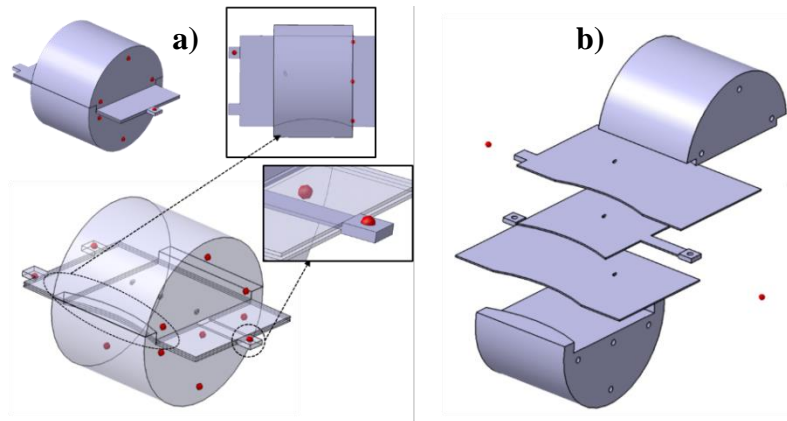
a) Ensamble y b) despiece del patrón prototipo
